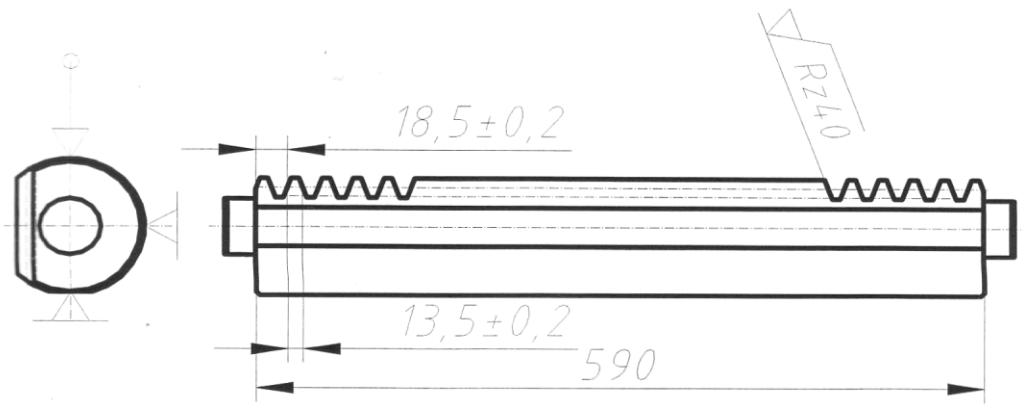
Ескіз обробки деталі операція №050
